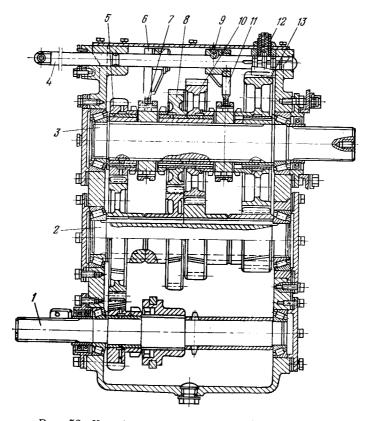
Коробка передач агрегата Азинмаш-32М: 1— приемный вал; 2— промежуточный вал; 3— выводной вал; 4— валик переключения передач; 5, 8, 10, 13— шестерни; 6, 11— вилки переключения; 7— муфта; 9— стонорный винт; 12— фиксатор
